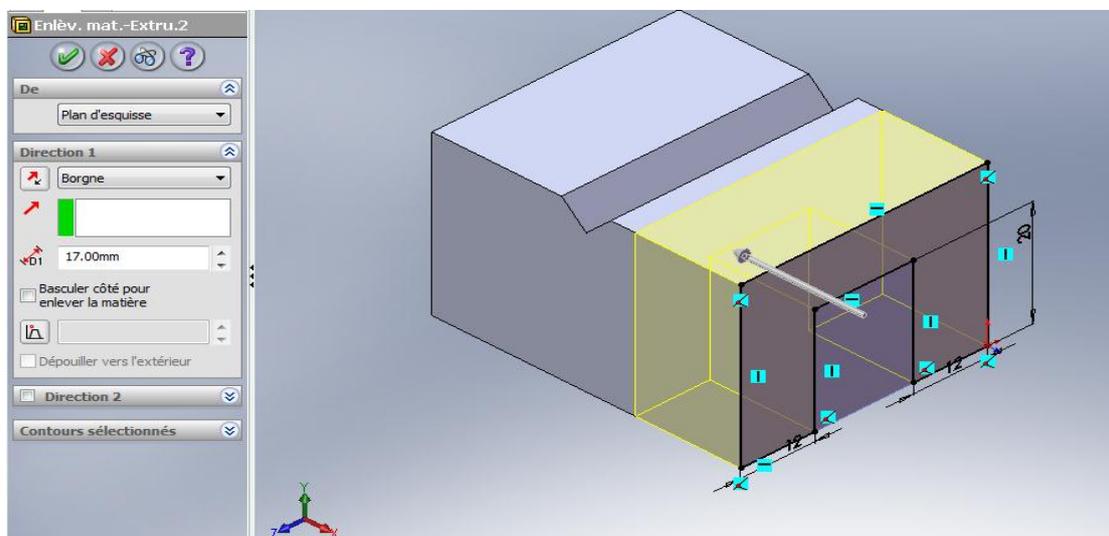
53.Enlèvement de matière sur le plan Droite.
